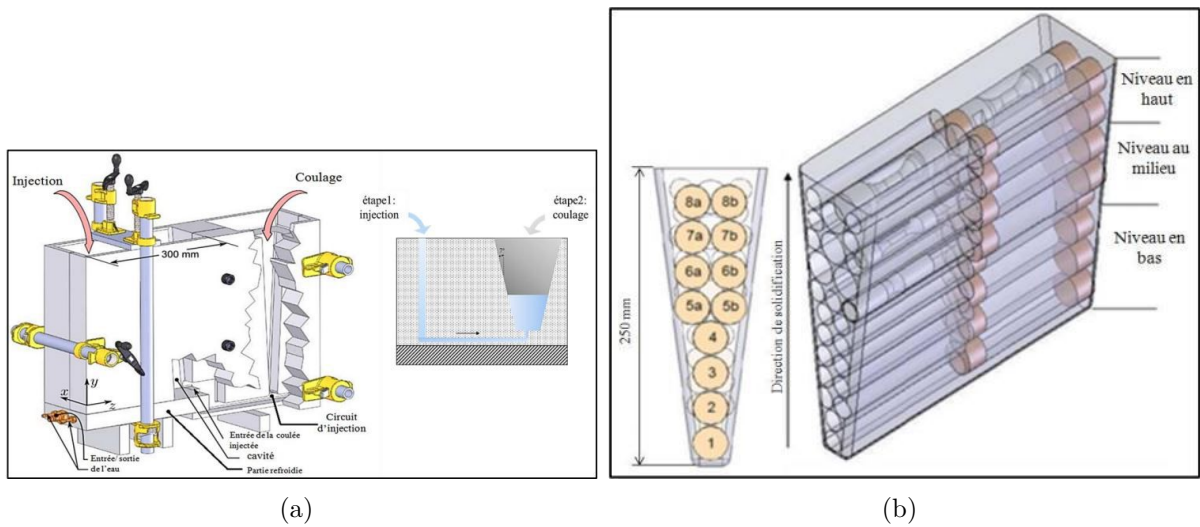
Modèle de coulée employé dans le travail de Houria et al. [2] : a) Dispositif expérimental de préparation de la coulée; b) géométrie de la coulée et emplacement des éprouvettes de fatigue
